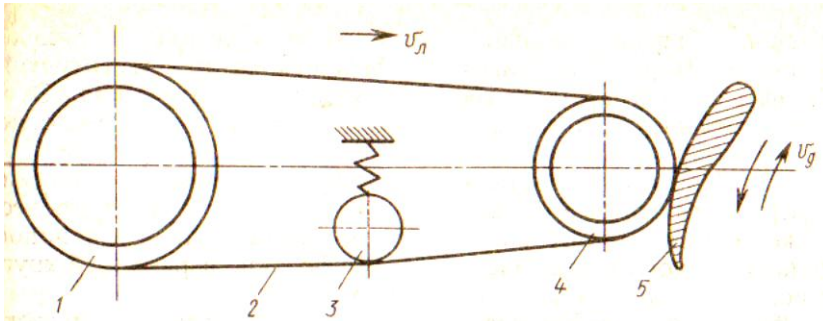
Схема ленточного шлифования: 1-ведущий диск; 2-лента; 3-натяжной диск; 4-ведомый диск; 5- деталь
